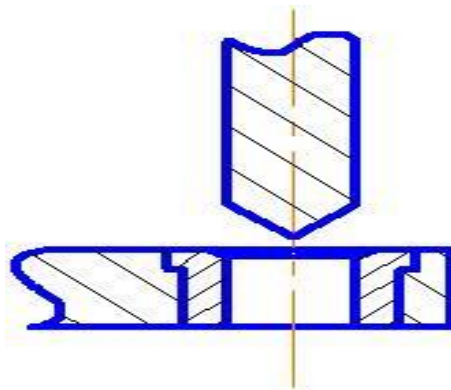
Зазор между сверлом и кондуктором втулкой кондуктора
